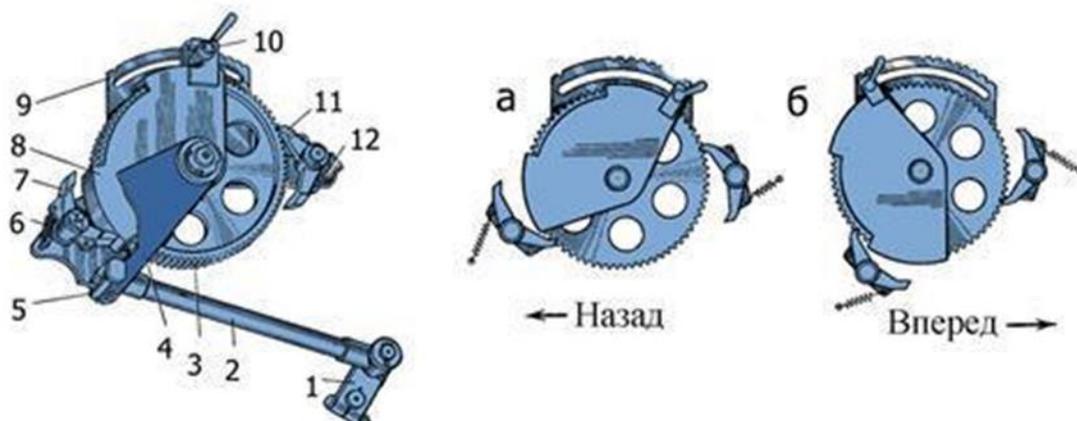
Кулісний механізм урухомника поперечного конвеєра КТУ-10А
